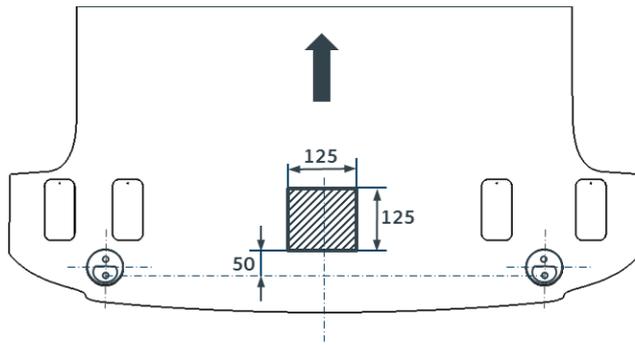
position et découpe pour aérateur de pavillon à l'arrière (cotes en mm)
